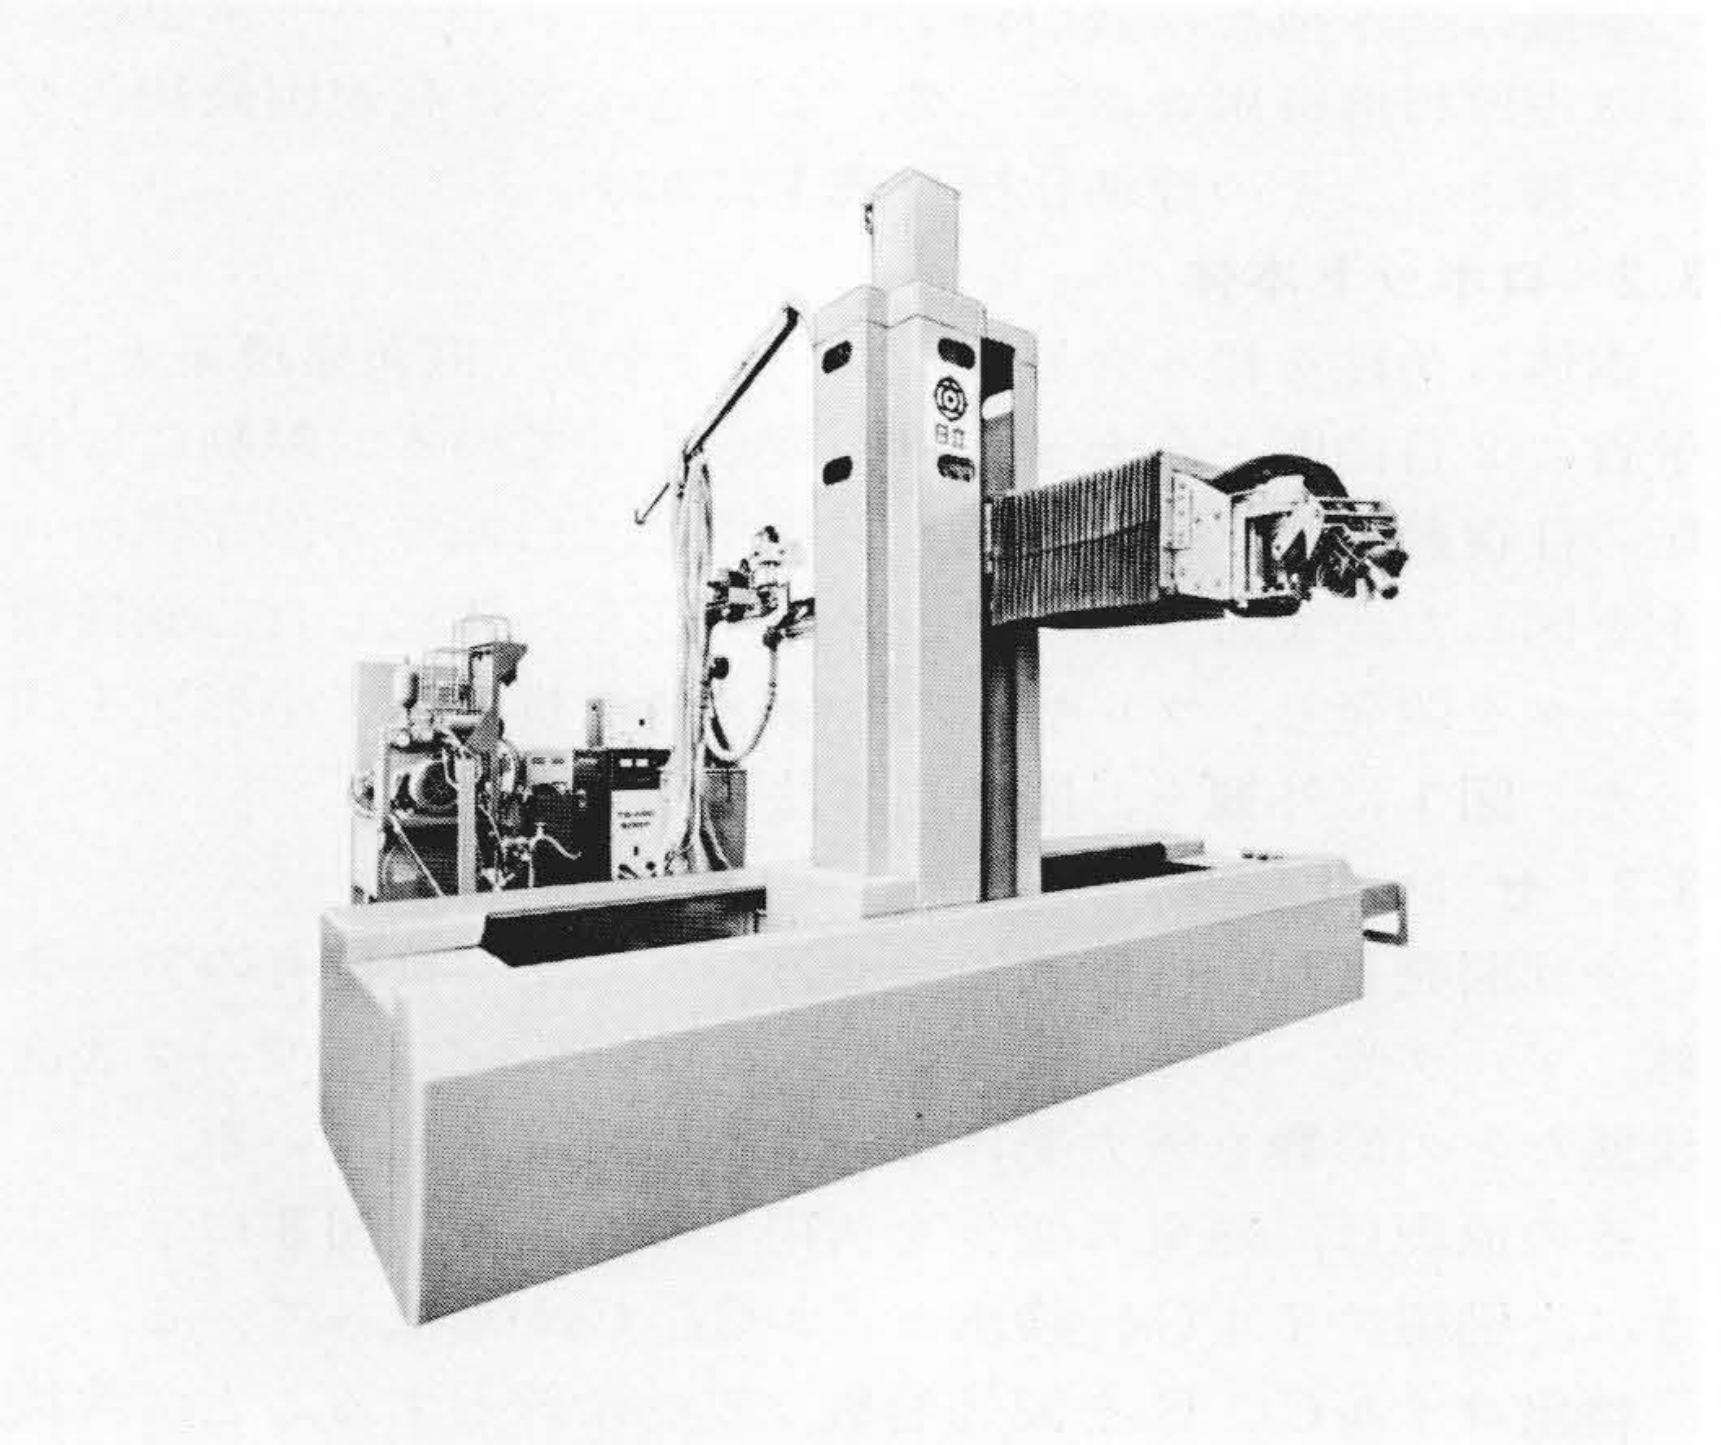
アーク溶接用ロボット「ミスターアロス」 ロボット後方は、左から油圧源、冷却水装置、溶接機電源、ケーブル用スタンド及びワイヤ引出し装置を配置した。
